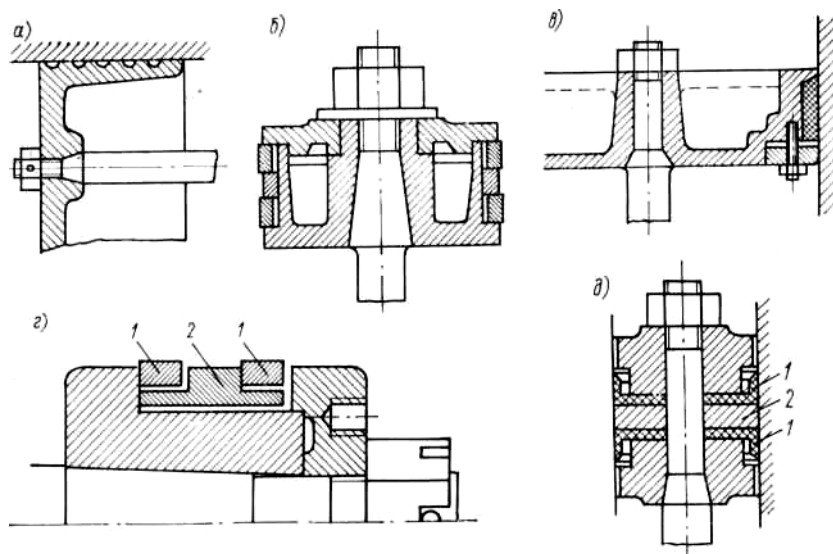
Дисковые поршни насосов: а — цельный; б — составной; в — с набивкой; г — с кольцами из эбонита; д — с кожаными манжетами
